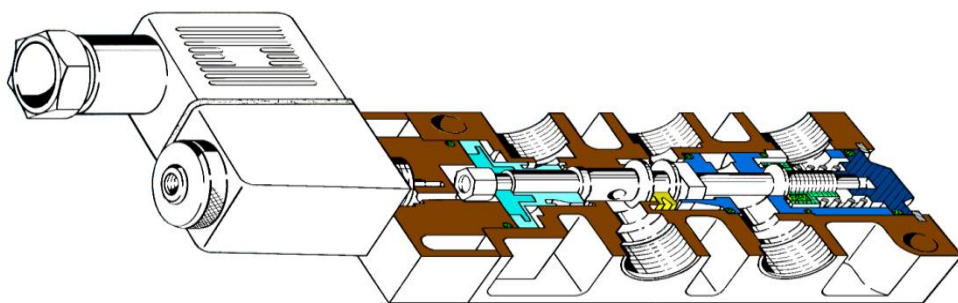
Imagen de Electroválvula construcción de asiento plano
